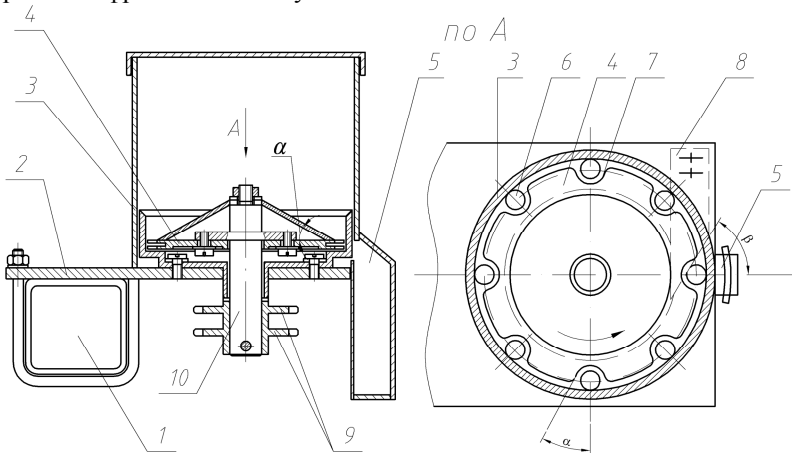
Конструктивно-технологічна схема сівалки точного висіву насіння: 1 – рама; 2 – корпус; 3 – бункер; 4 – висівний ділильний диск; 5 – насінепровід; 6 – насінини; 7 – комірки під насінини;
